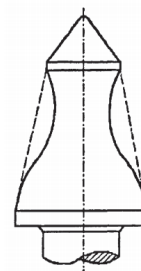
Форма износа поворотных резцов с твердосплавной вставкой грибовидной (ступенчатой) формы
